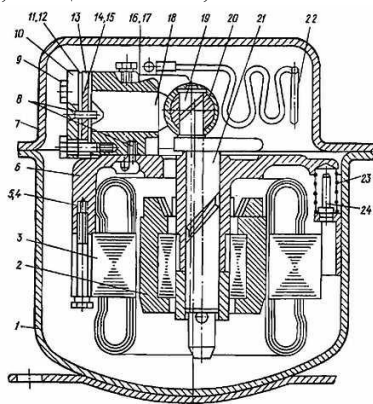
Конструкция кривошипно-кулисного мотор-компрессора (в сборе): 1 — герметичный кожух в сборе; 2 — ротор электродвигателя; 3 — статор электродвигателя; 4, 5 — винты; 6 — корпус компрессора; 7 — крышка кожуха; 8 — штифты; 9 — винт; 10 — головка цилиндра; 11 — прокладка клапана нагнетания; 12 — нагнетательный клапан; 13 — седло клапанов; 14 — клапан всасывающий; 15 — прокладка всасывающего клапана; 16, 17 — цилиндры; 18 — поршень; 19 — обойма; 20 — ползун; 21 — вал; 22 — трубка нагнетательная; 23 — пружина буферная; 24 — шпилька
